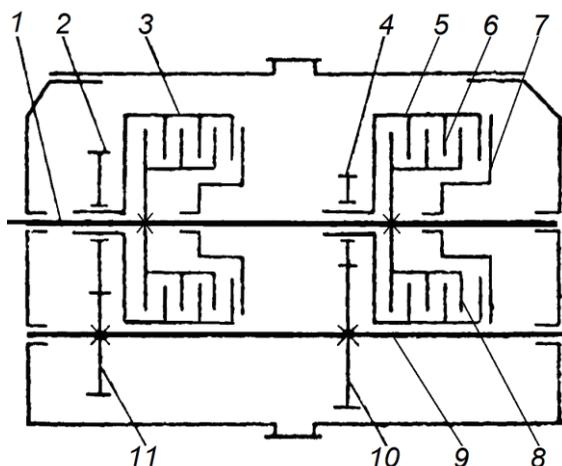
Схема коробки передач с шестернями постоянного зацепления
